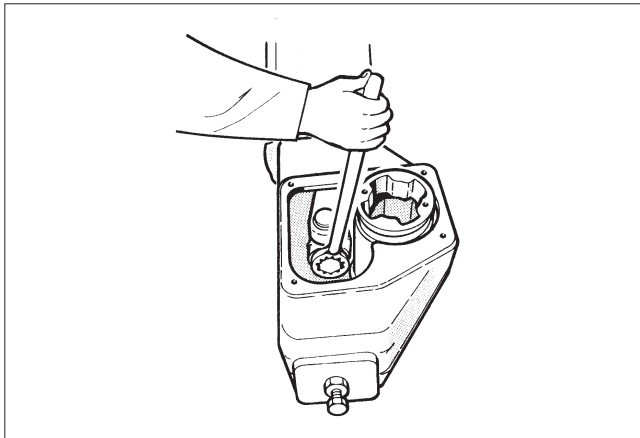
Öffnen der Befestigungsschraube der Lagereinheit des Stellantriebs
